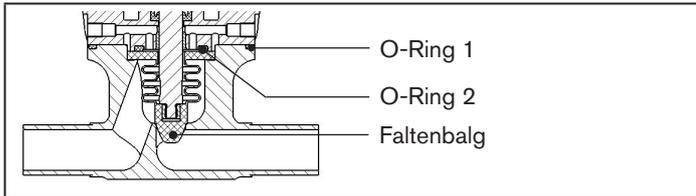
Detail (Ventilgehäuse - O-Ringe)
